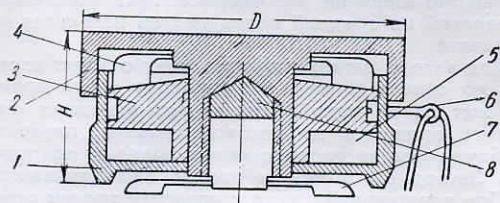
Общий вид тросикового устройства в разрезе: 1 — корпус, 2 — головка, 3 — барабан, 4 — пружина храповика, 5 — пружина барабана, 6 — тросик с петлей, 7 — пружина счетчика кадров, 8 — упор-вкладыш
